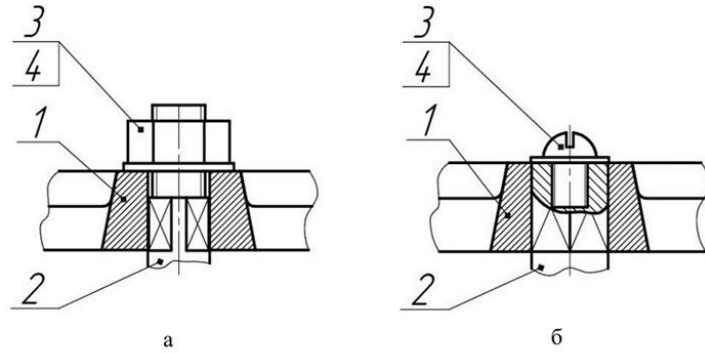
Способы соединения маховика и шпинделя с помощью: гайки и шайбы (а); винта и шайбы (б):
